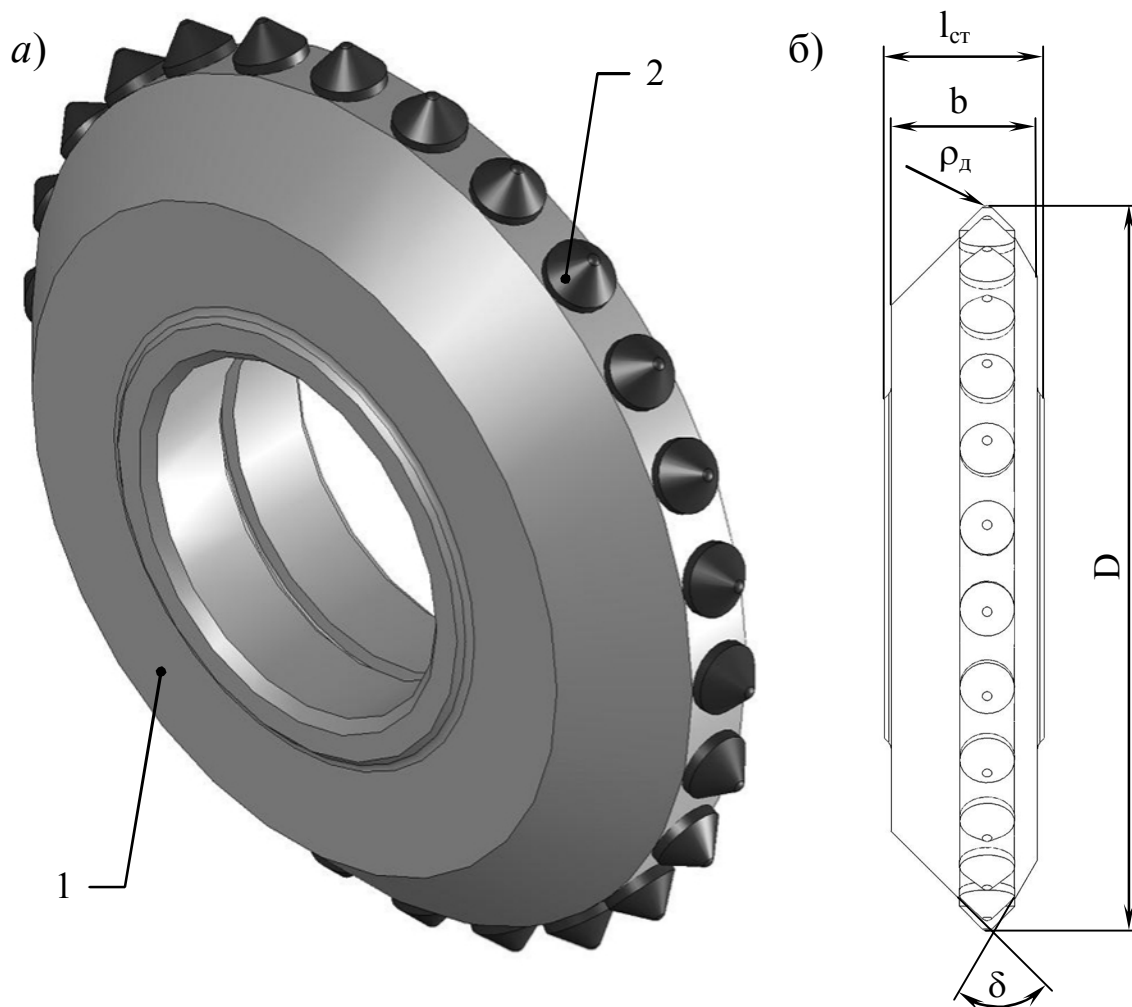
Вид (а) и параметры (б) режущего инструмента с вращающейся режущей частью
